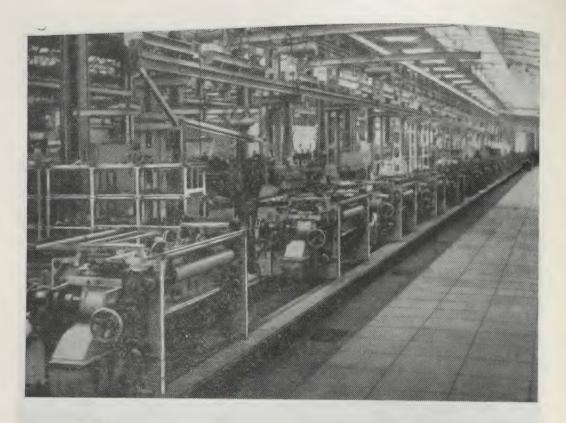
Конвейер окончательной сборки станка АТПР-100
